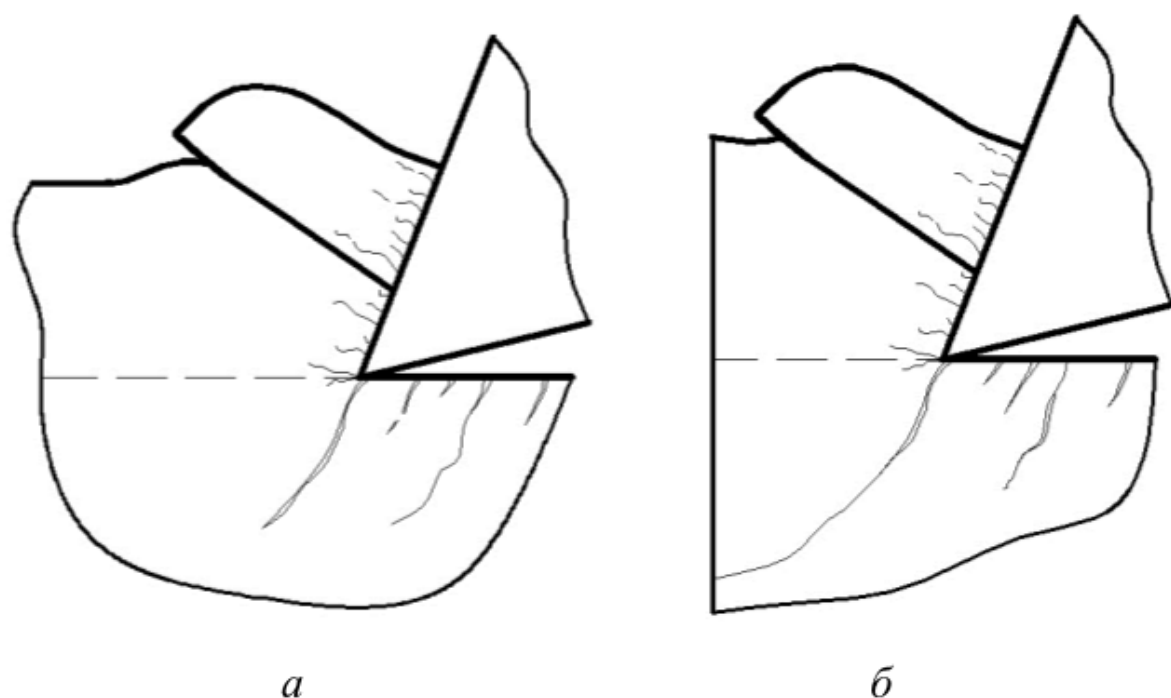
Образование макротрещин на обработанной поверхности (а) и сколов материала (б) на выходе режущего инструмента
